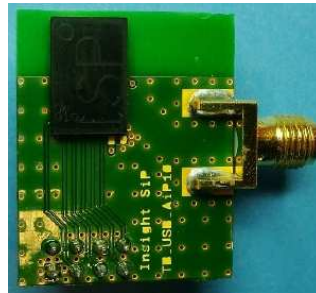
Module contenant uniquement la partie électronique, soudé sur un PCB de test
